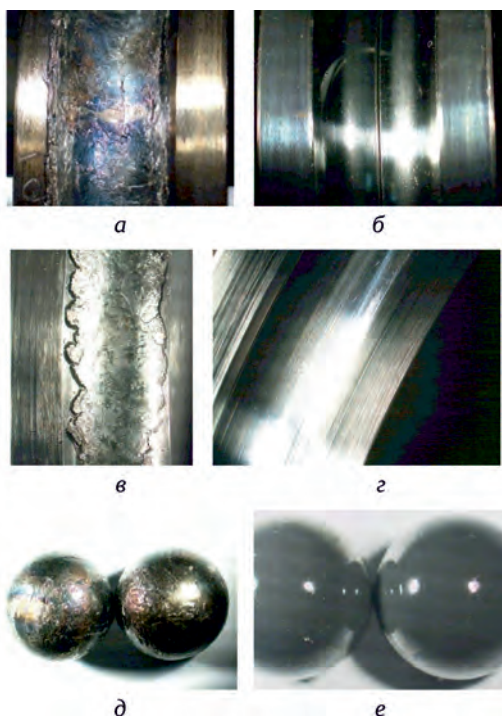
Состояние деталей стального и гибридного подшипников после испытаний с прекращением подачи масла: дорожки качения внутреннего кольца стального (а) и гибридного (б) подшипников; дорожка качения наружного кольца стального (в) и гибридного (г) подшипников; д – стальные тела качения; е – керамические тела качения
